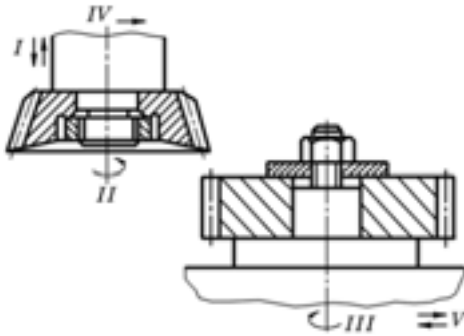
Схема нарізування зубів зубчастих коліс довбачами
